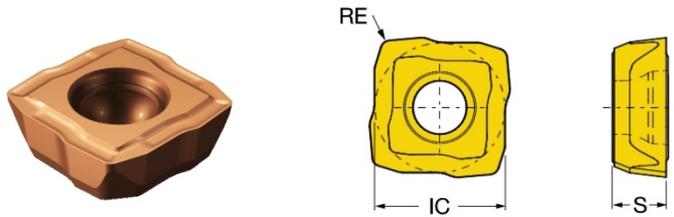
Режущая пластина для сверла CoroDrill® 880-04 03 W07H-P-GR
